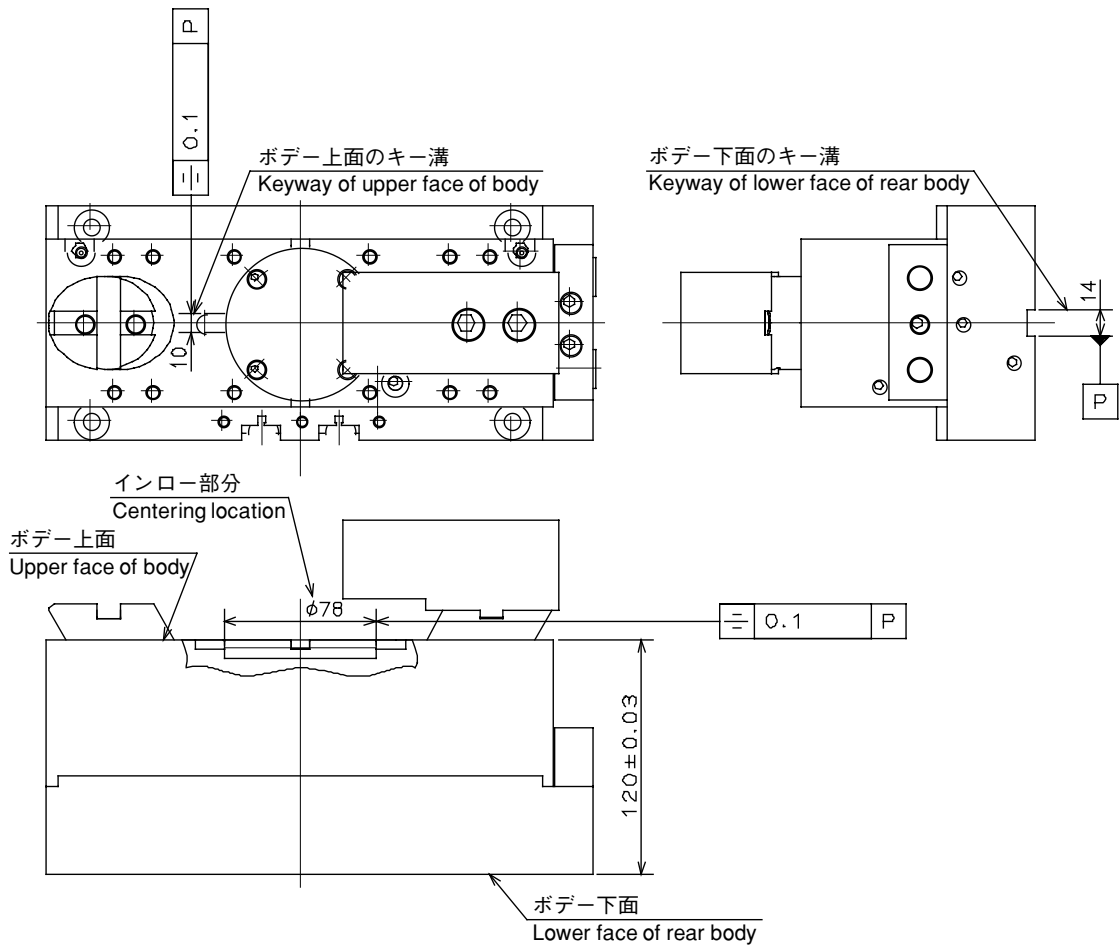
検査詳細図 Detailed Inspection Drawing
